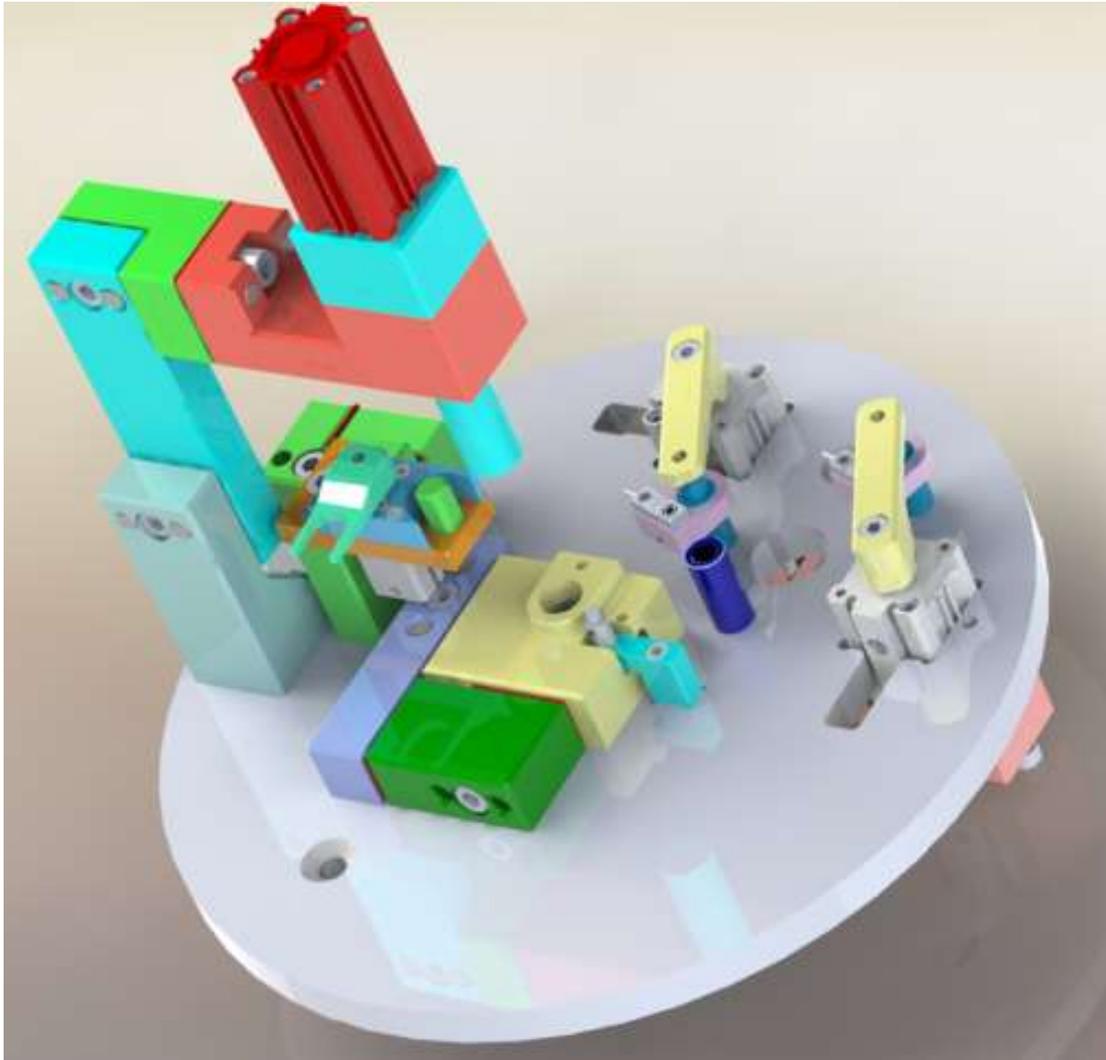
Diseño de Montadura del fixture PM7RH.
